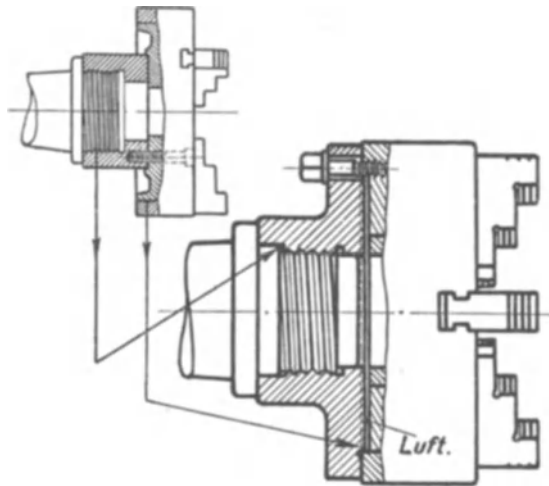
Futterflansch. Veraltete und neuzeitliche Befestigung.
